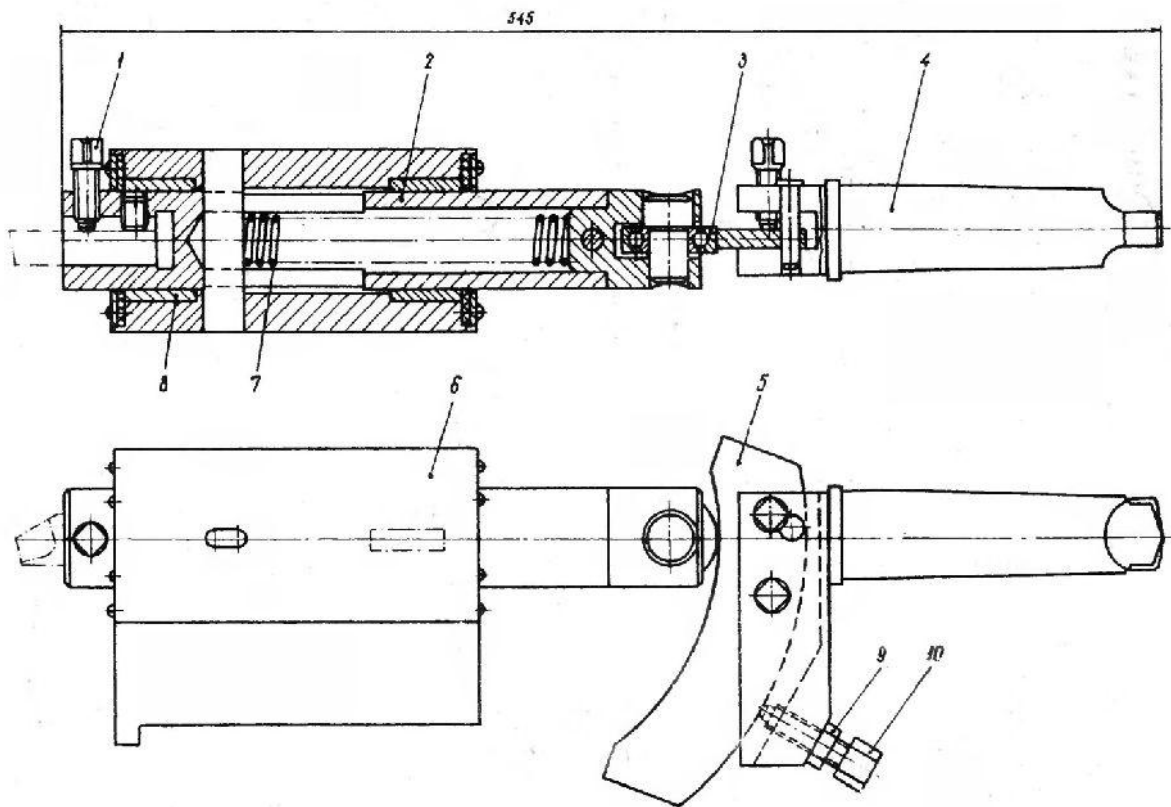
Приспособление для точения сферических поверхностей
